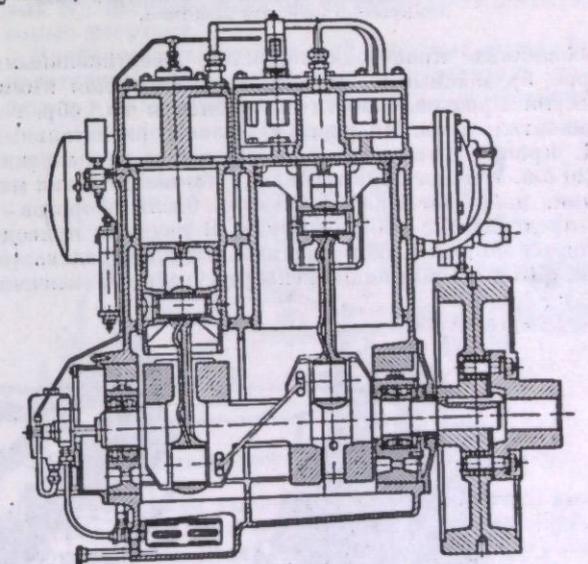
Вертикальный поршневой двухступенчатый компрессор простого действия.
